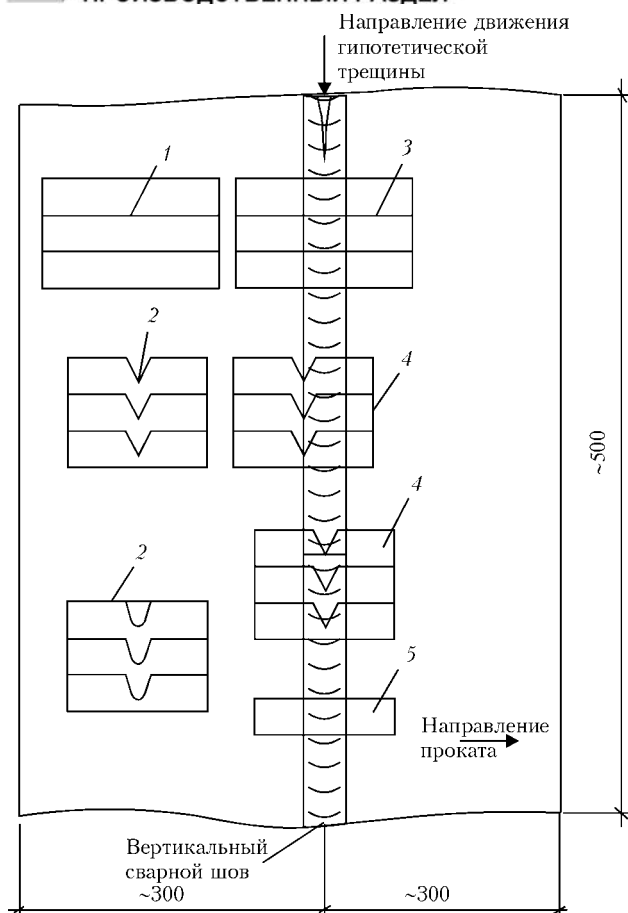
Схема расположения на пластине-заготовке со сварным швом образцов: 1 — для механических испытаний основного металла; 2 — с надрезами *KCU* и *KCV* для определения ударной вязкости; 3 — для механических испытаний шва; 4 — с надрезами *KCU* и *KCV* для определения ударной вязкости металла шва и ЗТВ; 5 — для металлографических исследований
